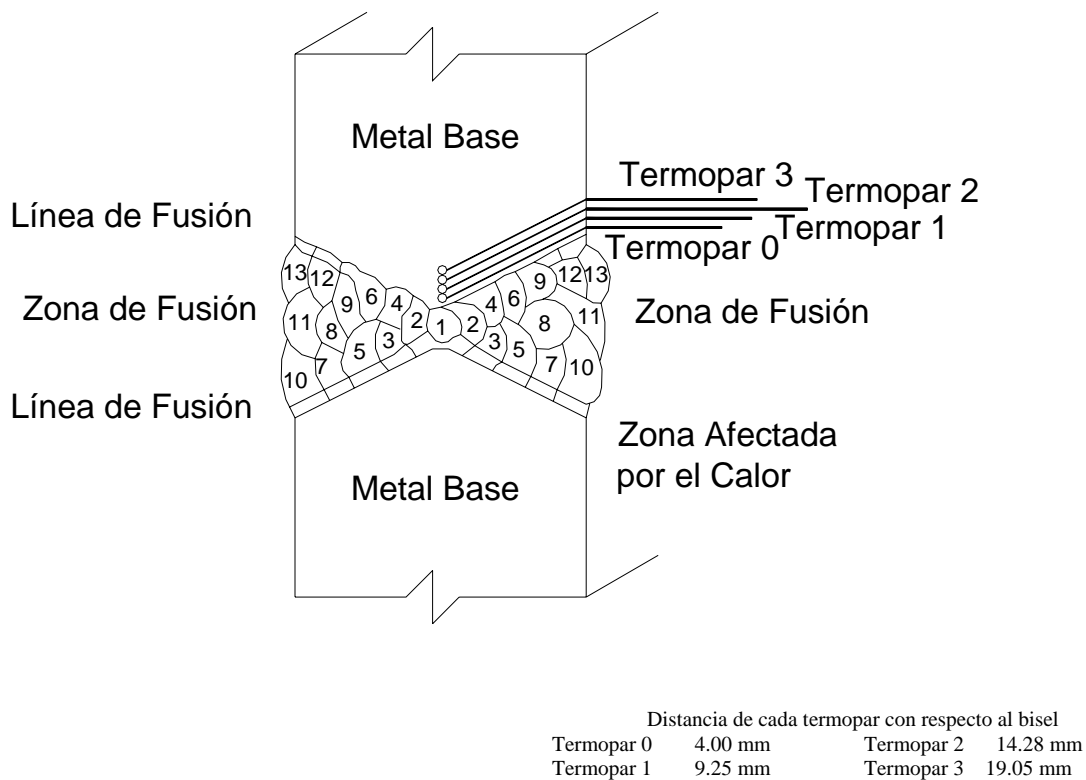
Esquema que muestra los 26 cordones de soldadura aplicados para la unión de las placas, así como la localización de los 4 termopares.
